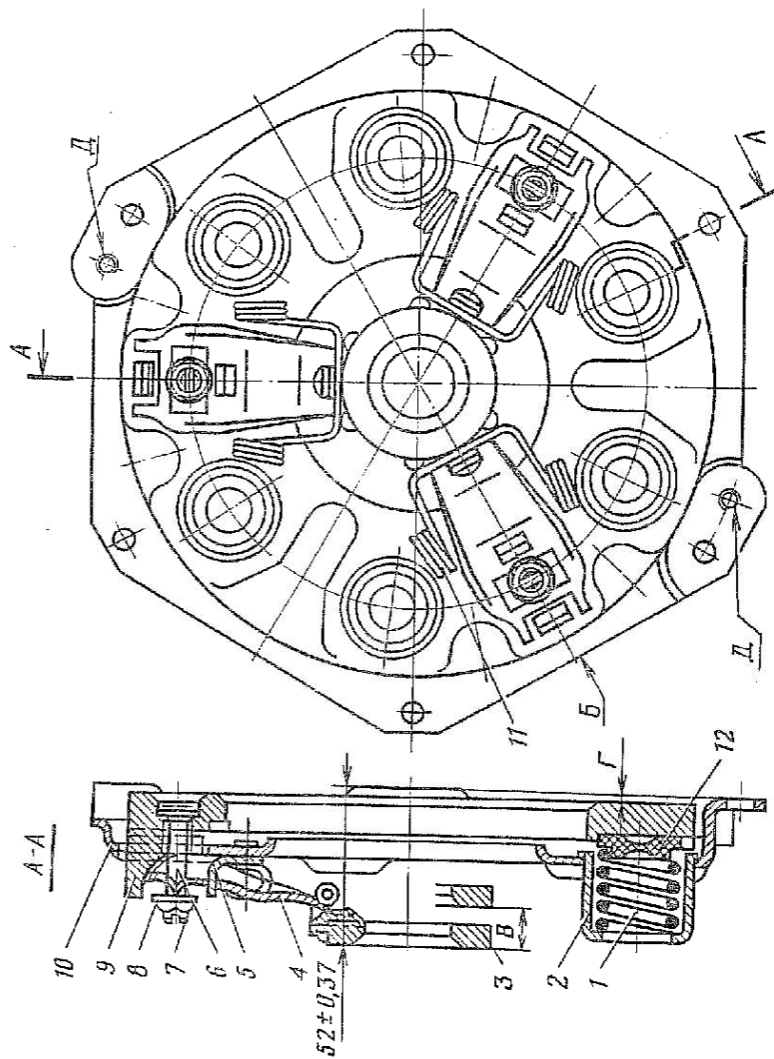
Нажимной диск сцепления с кожухом в сборе:
